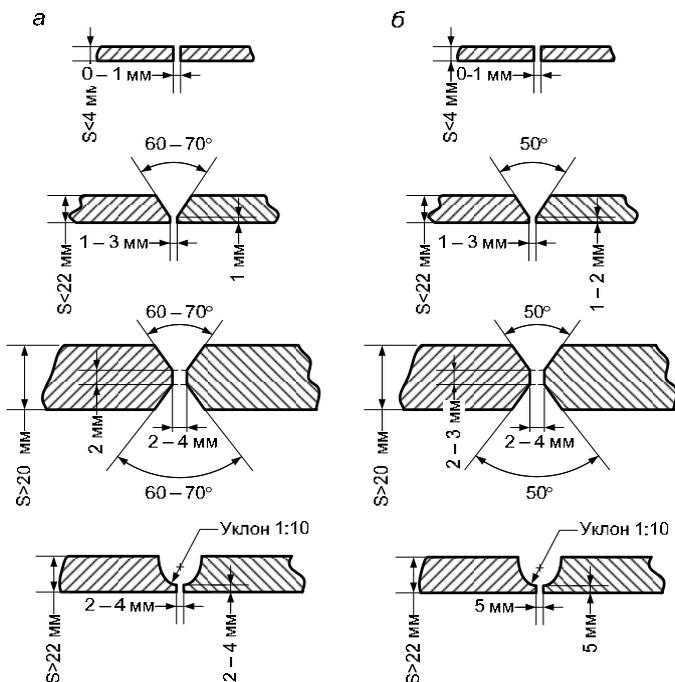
Подготовка кромок для ручной и автоматической сварки под слоем флюса:
